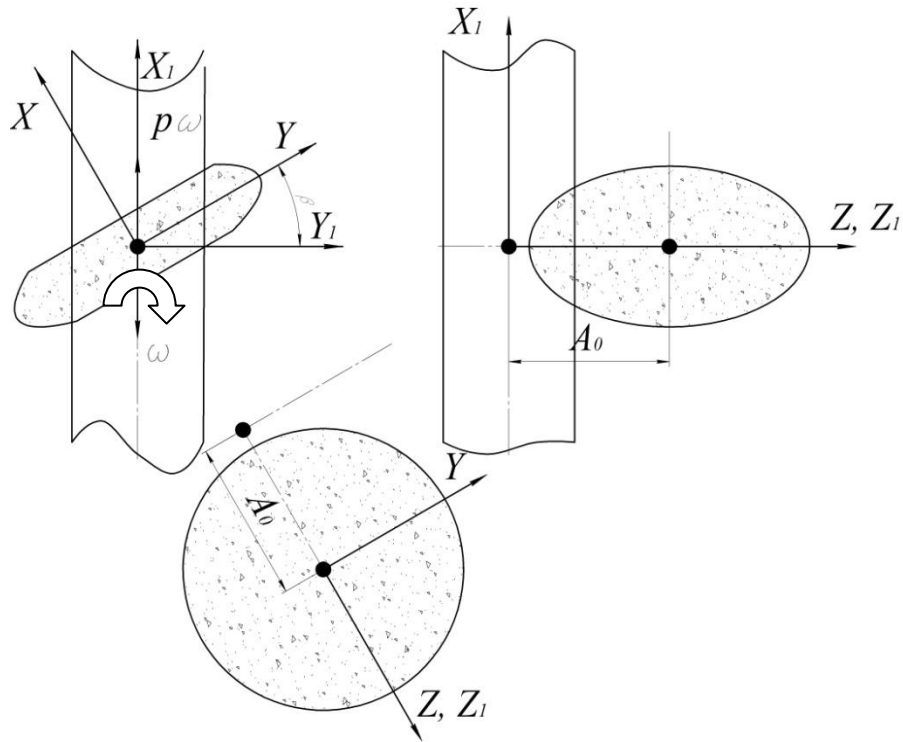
Розрахункова схема формоутворення фасонною поверхню обертання гвинтової поверхні
